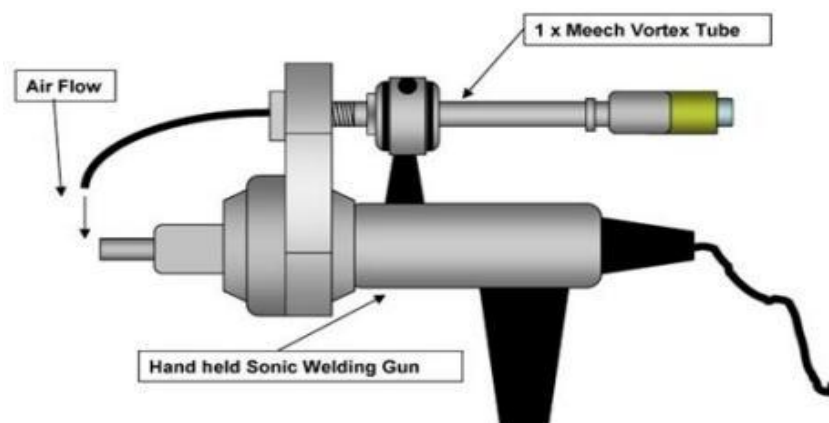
Pistolet de soudage sonore avec intégration d'un tube à vortex.
